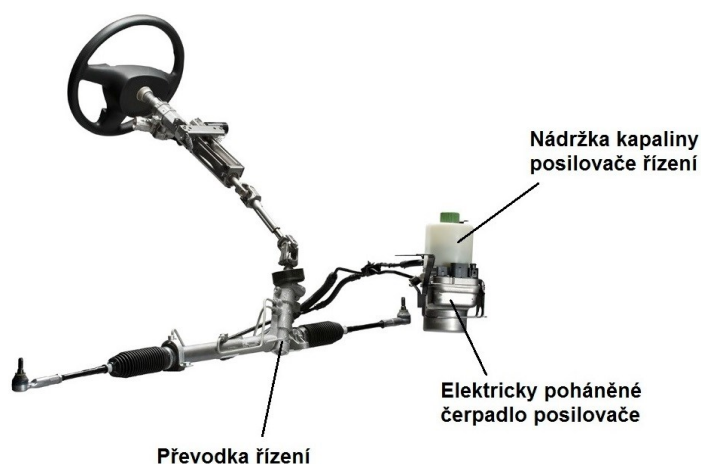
Hydraulický posilovač s hřebenovou převodkou řízení [5]
